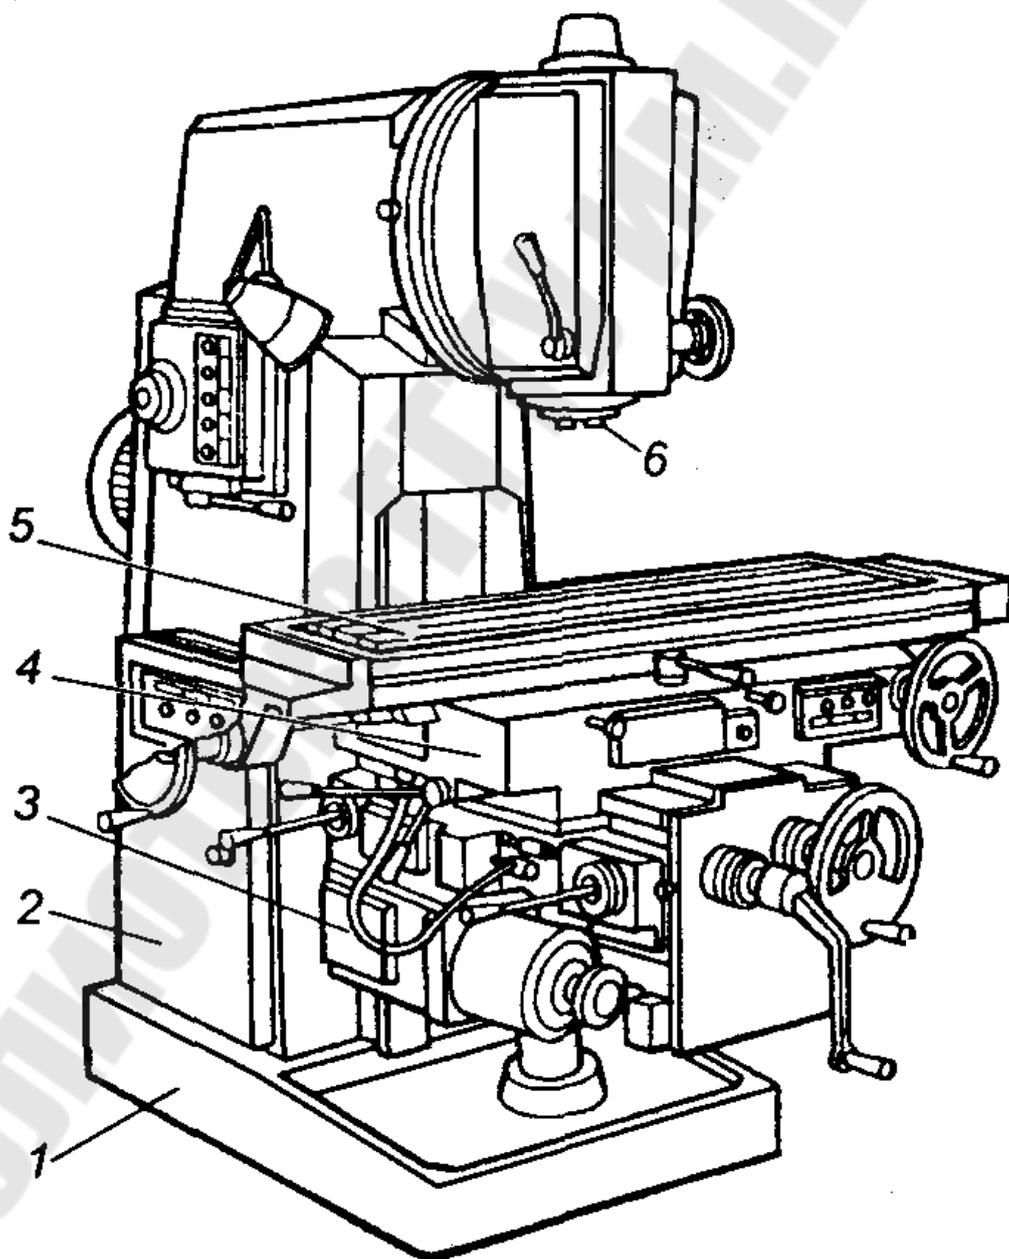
Общий вид вертикально-фрезерного станка
